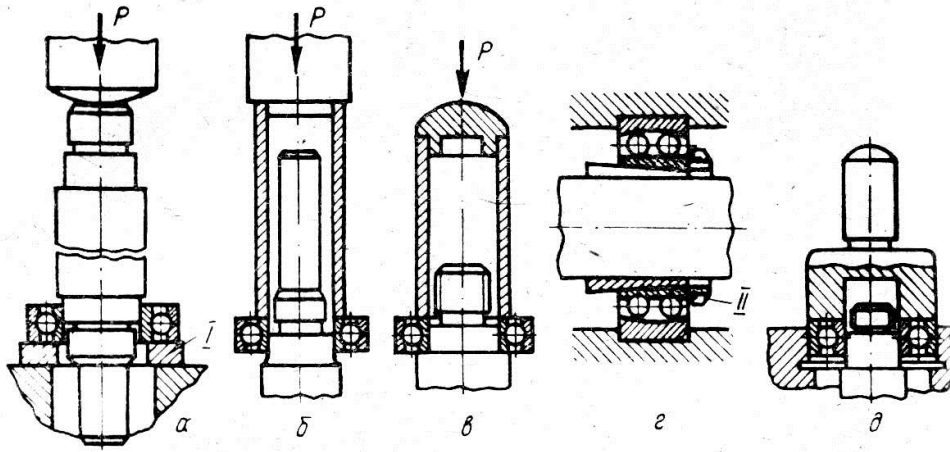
Установка підшипників кочення на вал і в корпус деталі:
